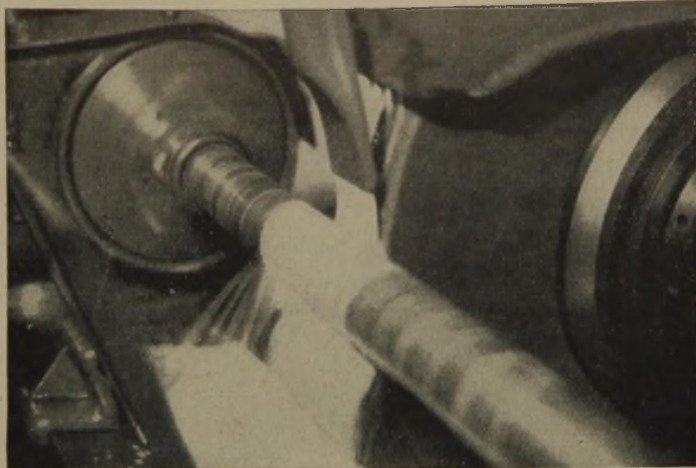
Bei breiter Tülle der Kühlleitung und starkem Kühlstrom wird das Kühlmittel richtig zugeführt
